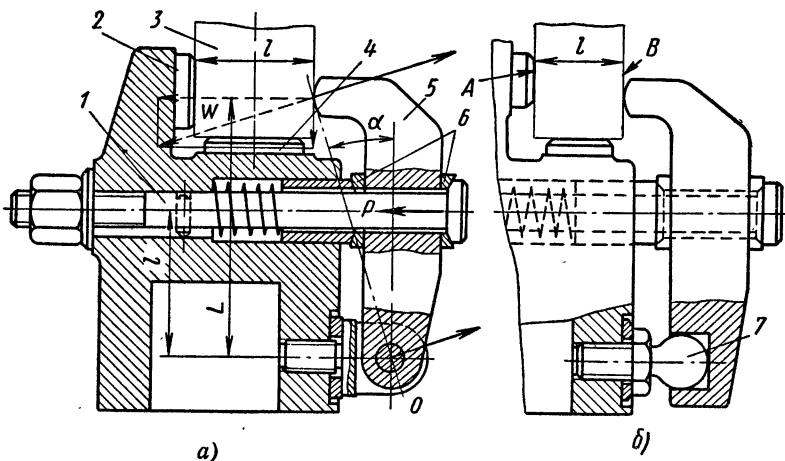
Прихваты, обеспечивающие зажим детали в двух направлениях
